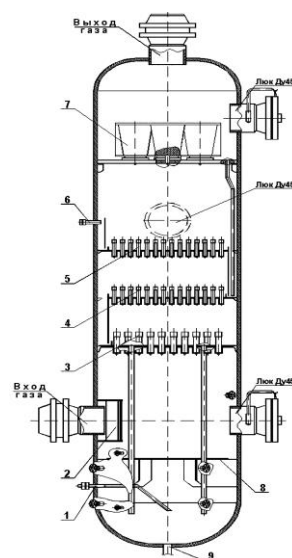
Схема сепаратора штатной конструкции (1 – штуцер слива жидкости из кубовой части; 2 – тангенциальное входное устройство с сетчатым коагулятором; 3 – тарелка с прямоточными сепарационными центробежными элементами типа; 4, 5 – тарелка с центробежными массообменными элементами типа; 6 – штуцер для подачи в аппарат промывочной жидкости; 7 – секция с сетчатыми сепарационными элементами типа; 8 – защитный лист; 9 – штуцер дренажа).
